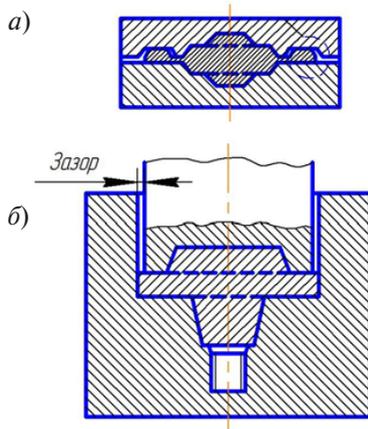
Схема открытой (а) и закрытой (б) штамповки
